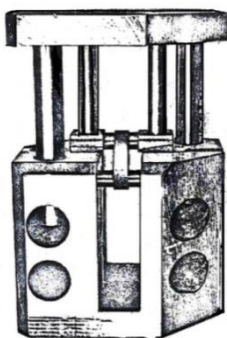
Реверсор для испытаний кольцевых образцов на разрыв
